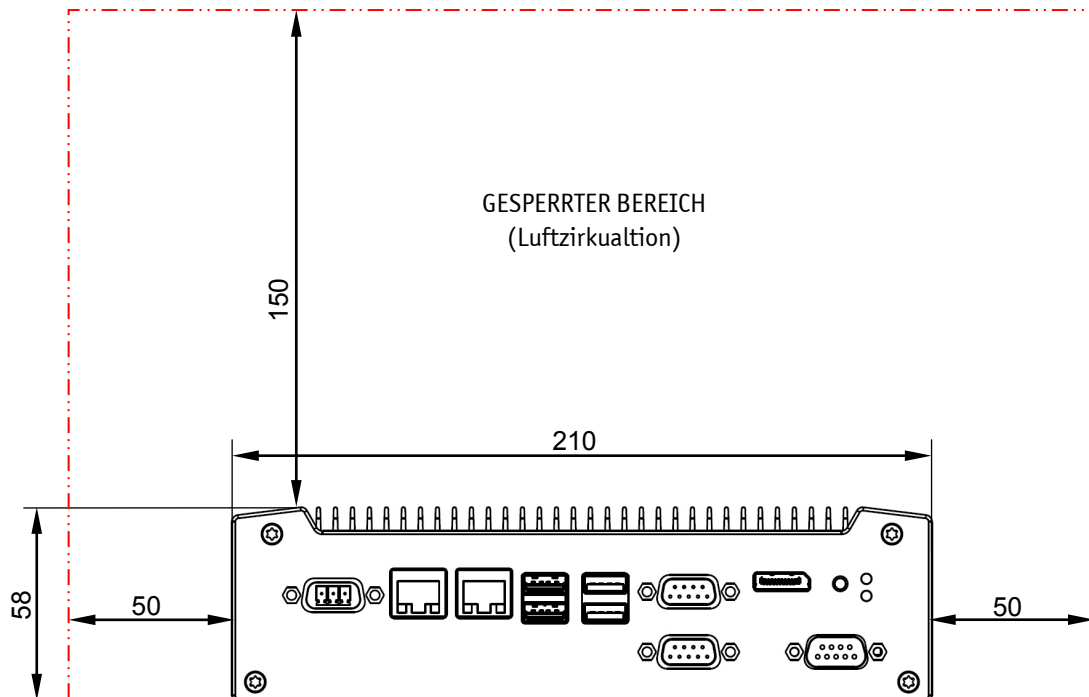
Maßangaben in der Frontansicht (Hutschienenmontage)
